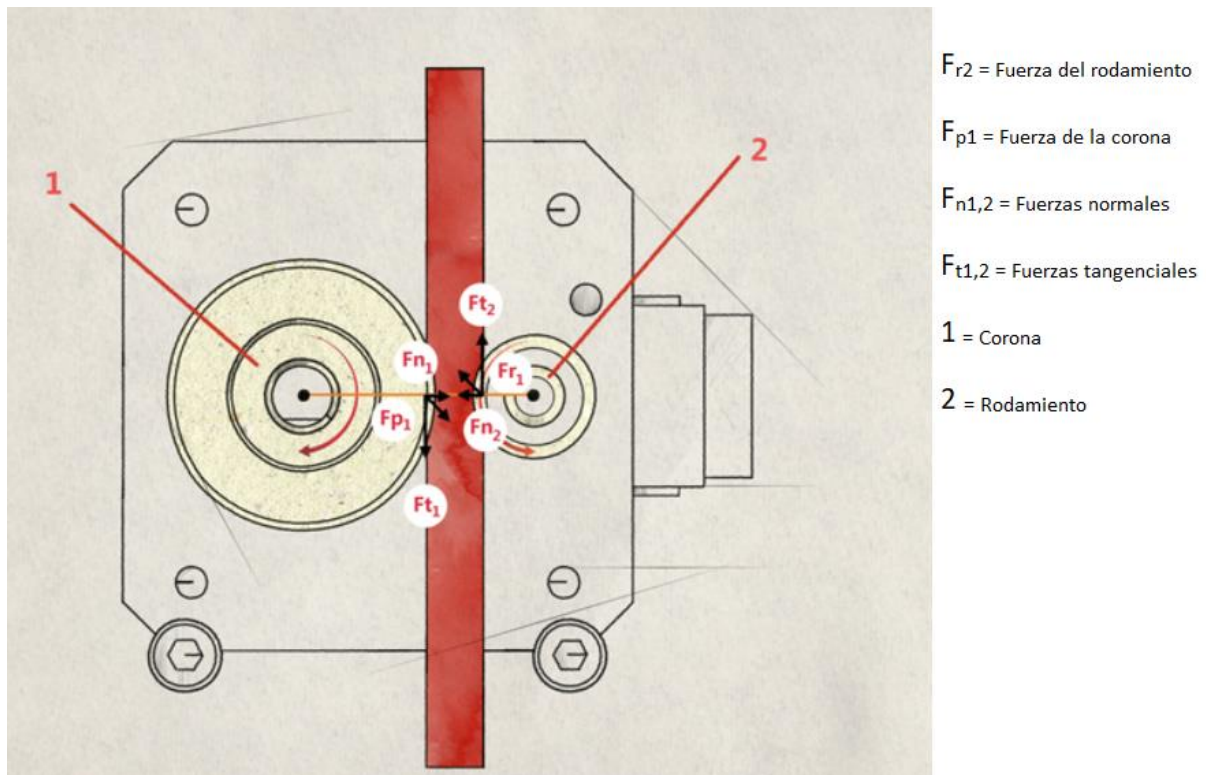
Distribución de fuerzas. Engranaje-Rodamiento.
